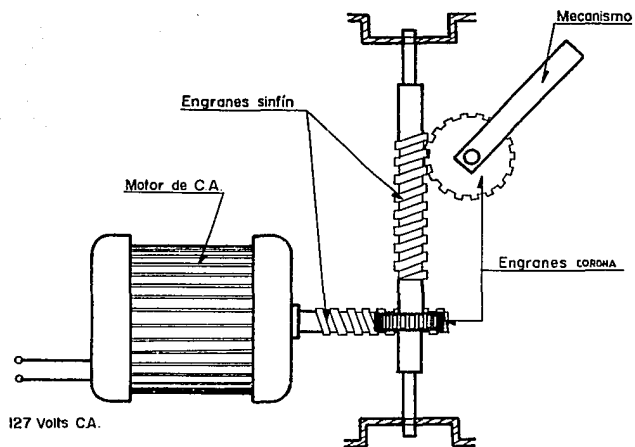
MOTOR DE C.A Y MECANISMO DE ENGRANES SINFÍN - CORONA
